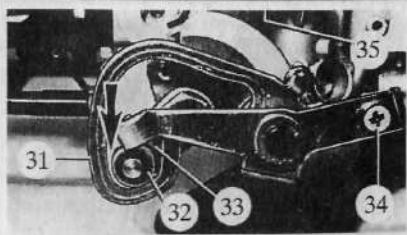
Регулировка приводного рычага газа на карбюраторе для автомобиля с механической коробкой передач и ручным управлением: 31 — кулиса; 32 — ролик; 33 — коромысло; 34 — стяжной винт; 35 — упорный винт рычага дроссельной заслонки. Стрелка указывает на место возможного соприкосновения ролика и ручья кулисы.
